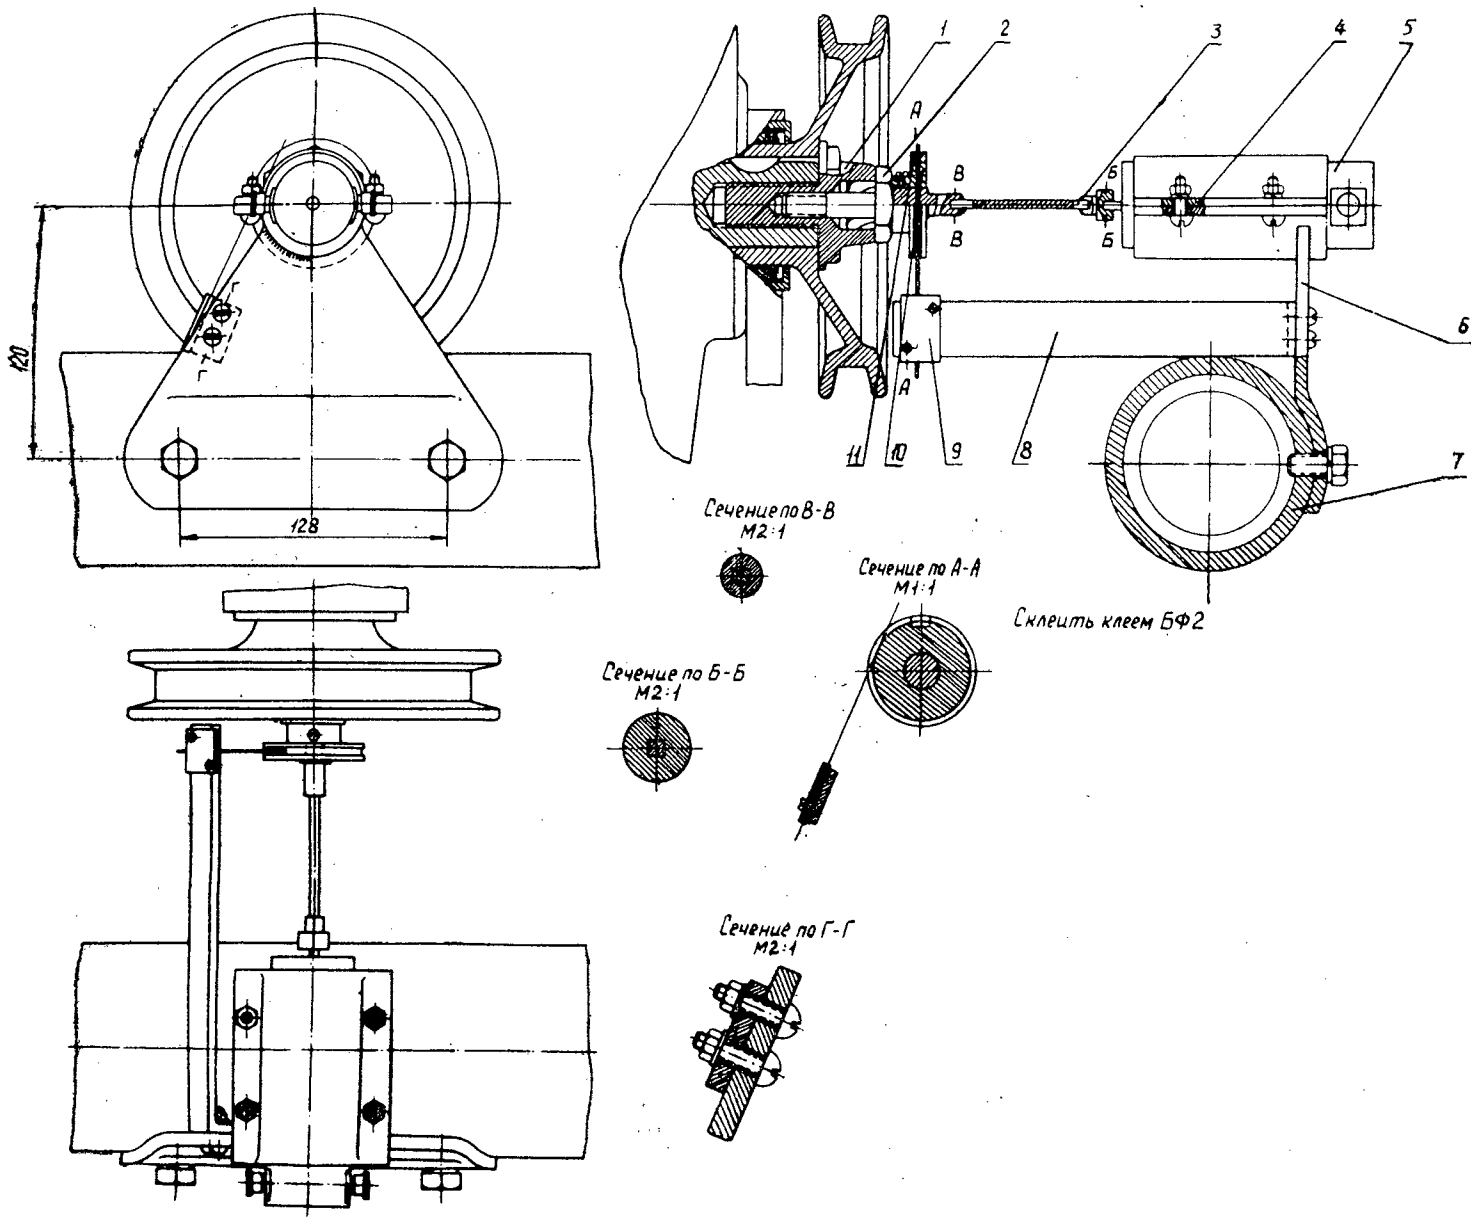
Схема установки преобразователя отметки верхней мертвой точки двигателя и тахогенератора на коленчатом валу.
